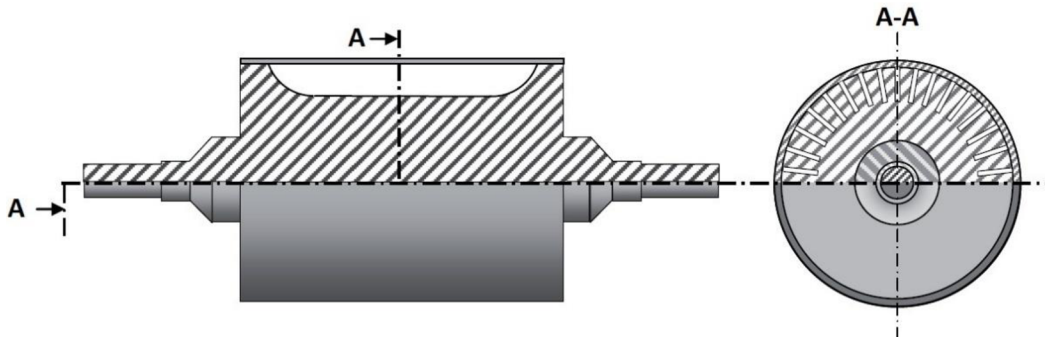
2 Vyfrézované axiální drážky do plného rotoru [2]
